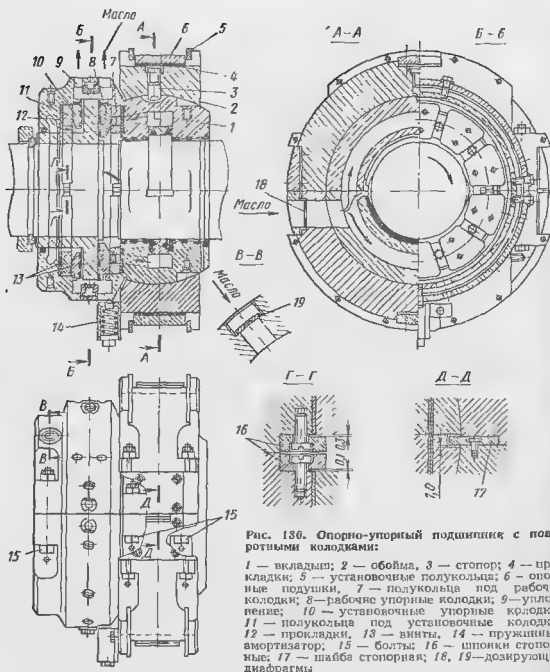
Опорно-упорный подшипник с поворотными колодками:
